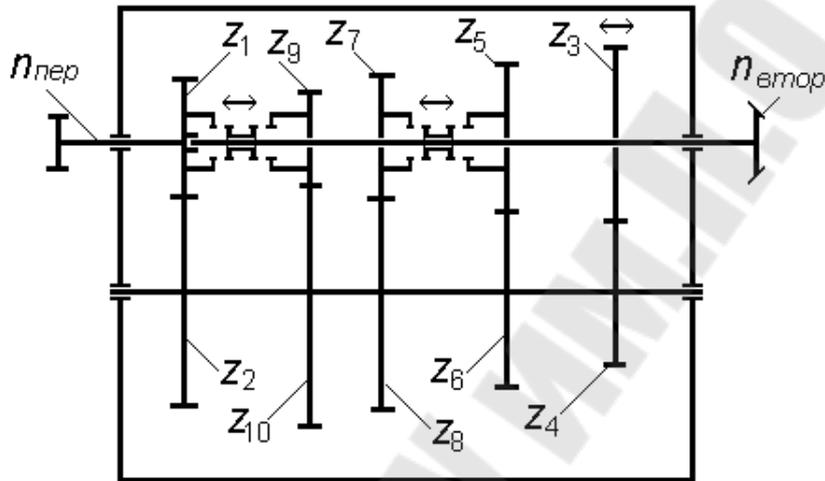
Кинематическая схема пятиступенчатой коробки передач
